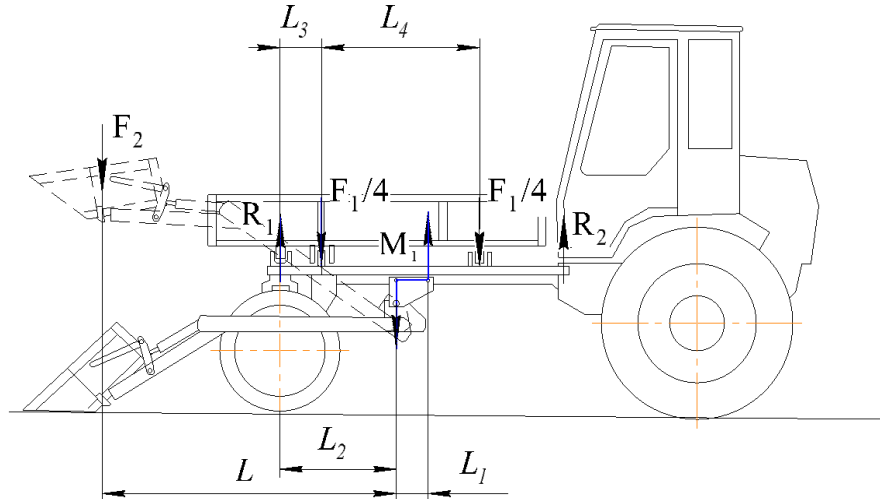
Розрахункова схема навантаження фронтального навантажувача
